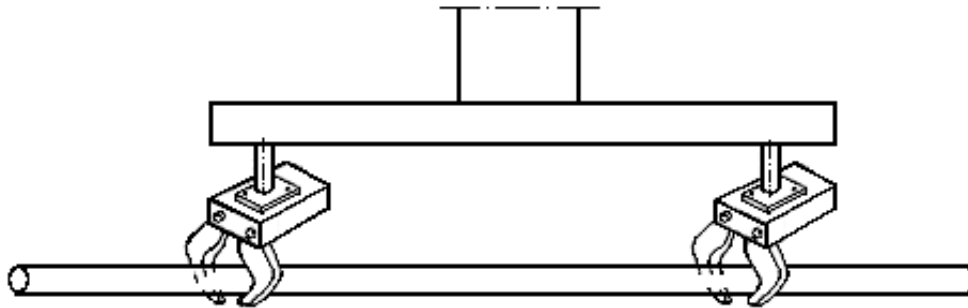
Схема сдвоенного клещевого захвата для длинномерных прутков
